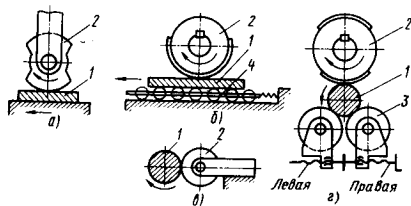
Схемы клеймения деталей накатыванием: а и б — плоских деталей на поперечно-строгальном и горизонтально-фрезерном станках; в и г — цилиндрических деталей на токарном и горизонтально-фрезерном станках; 1 — деталь; 2 — накатный ролик; 3 — опорные ролики; 4 — каретка
